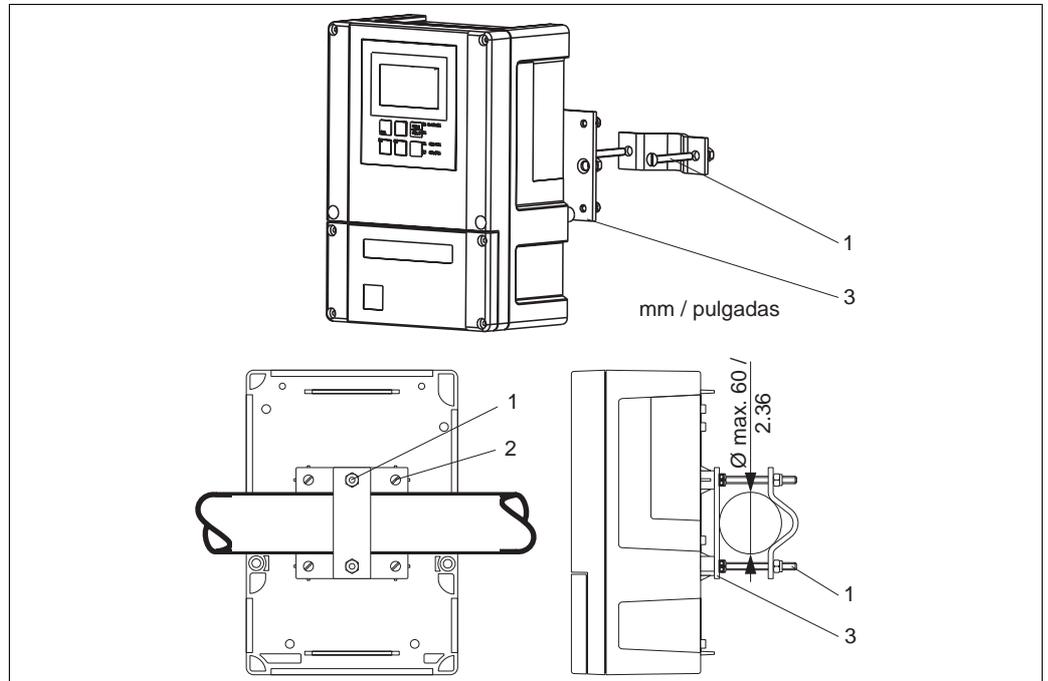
Montaje del equipo de campo en una tubería cilíndrica
